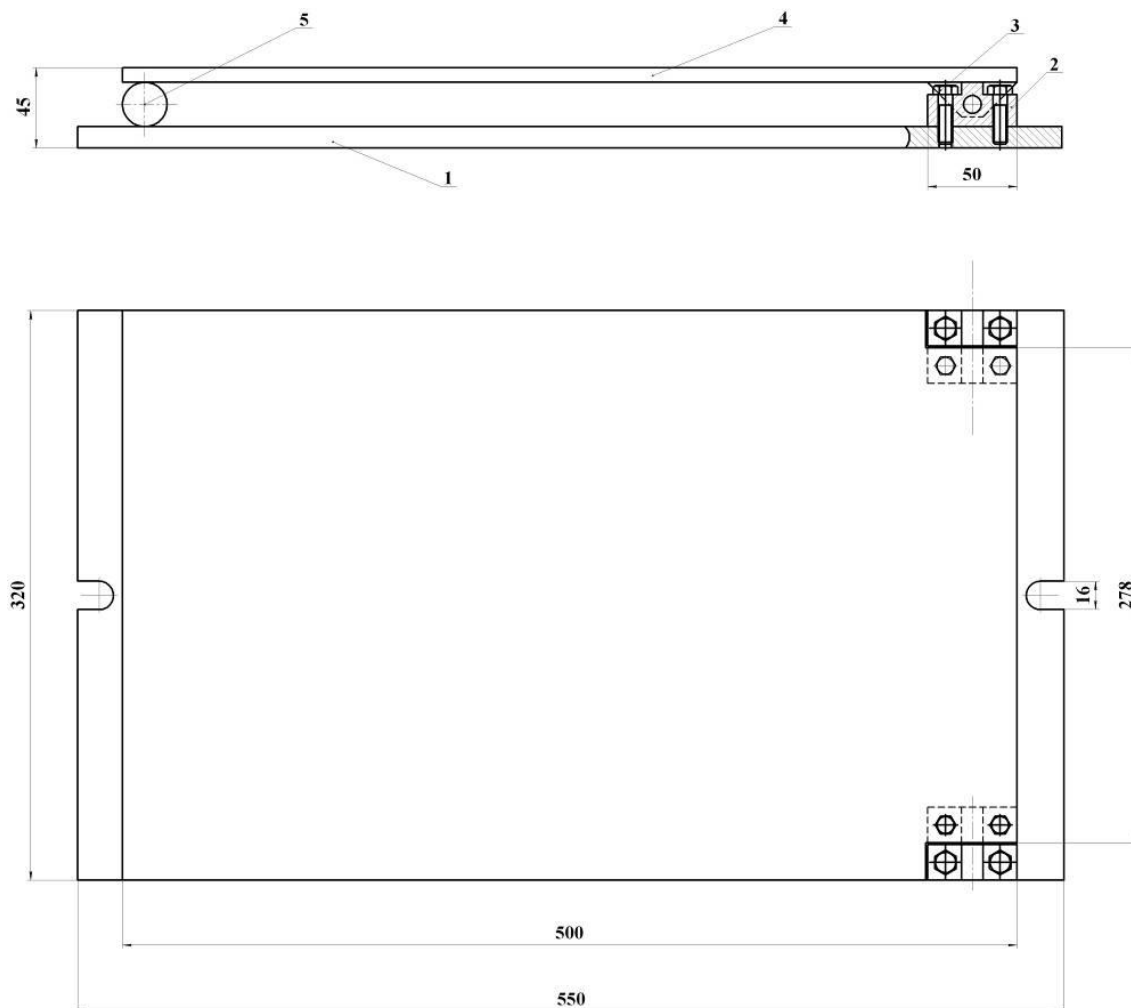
Конструктивная схема приспособления для закрепления и последующей механической обработки стыковых поверхностей резиноканевых конвейерных лент
